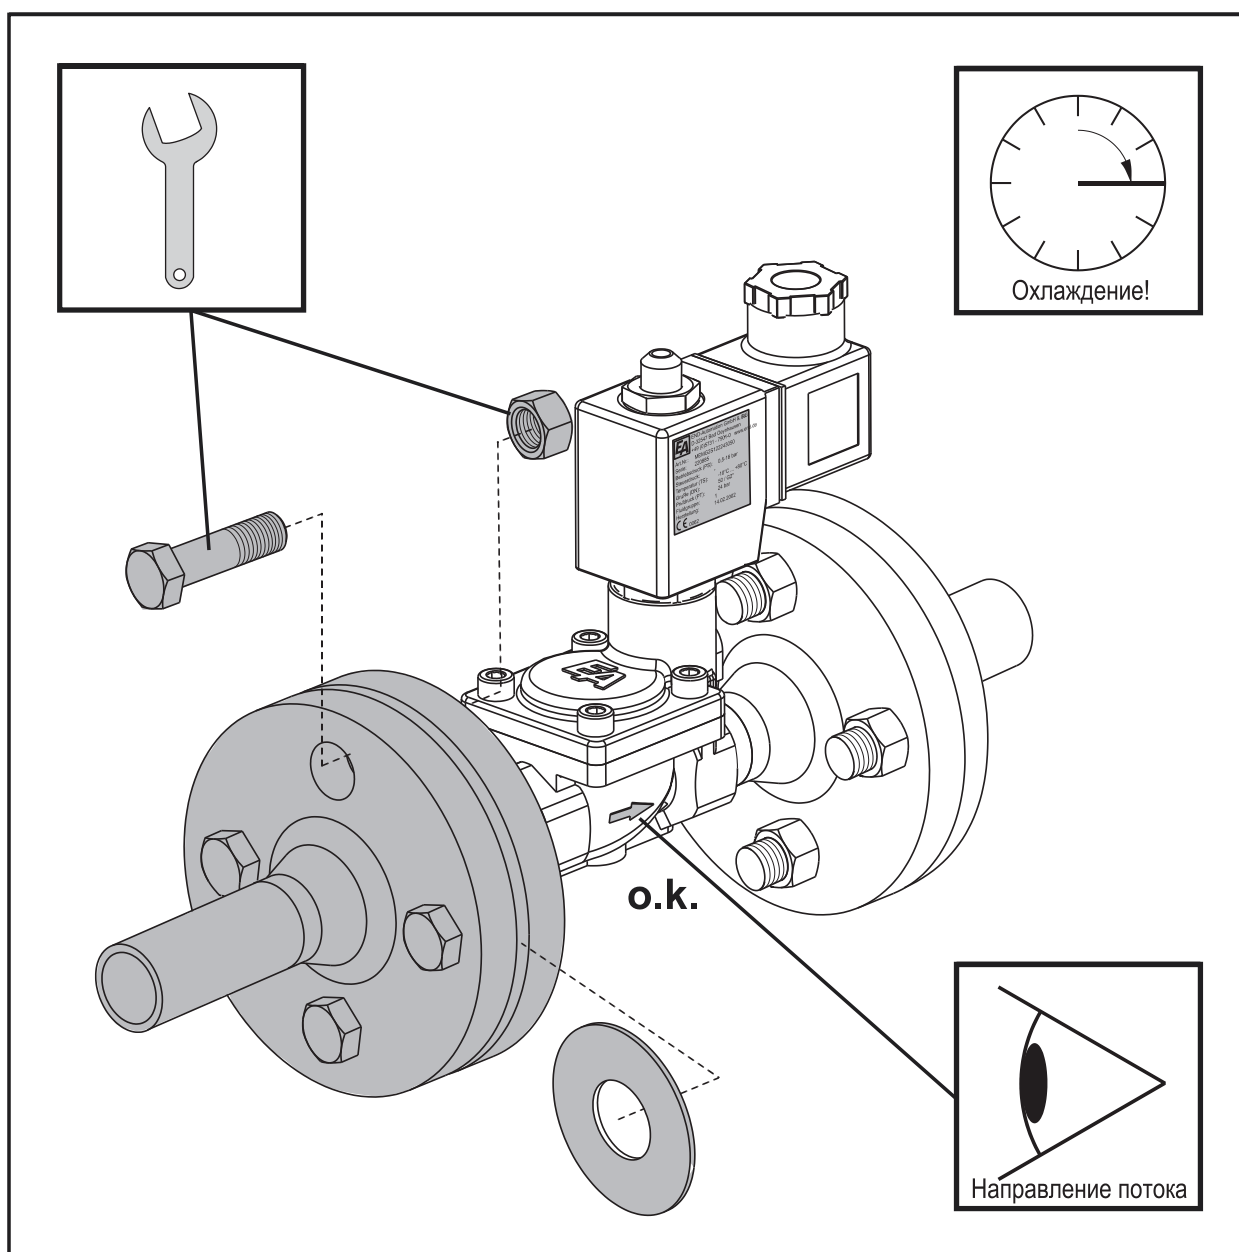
Монтаж/демонтаж – фланцевое соединение
